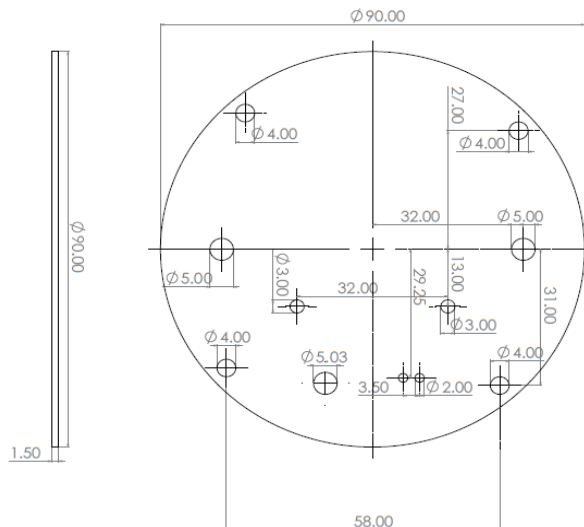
Placa intermedia, vista lateral y vista planta.
